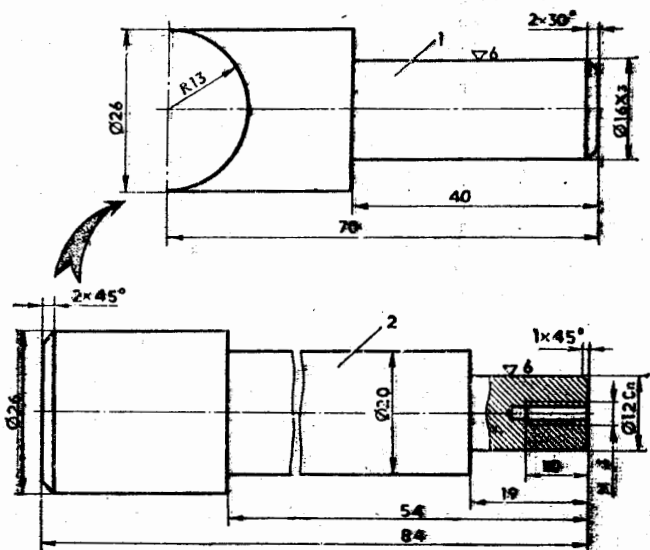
Конструкция шкворня колеса: 1 — палец, 2 — полуось.
